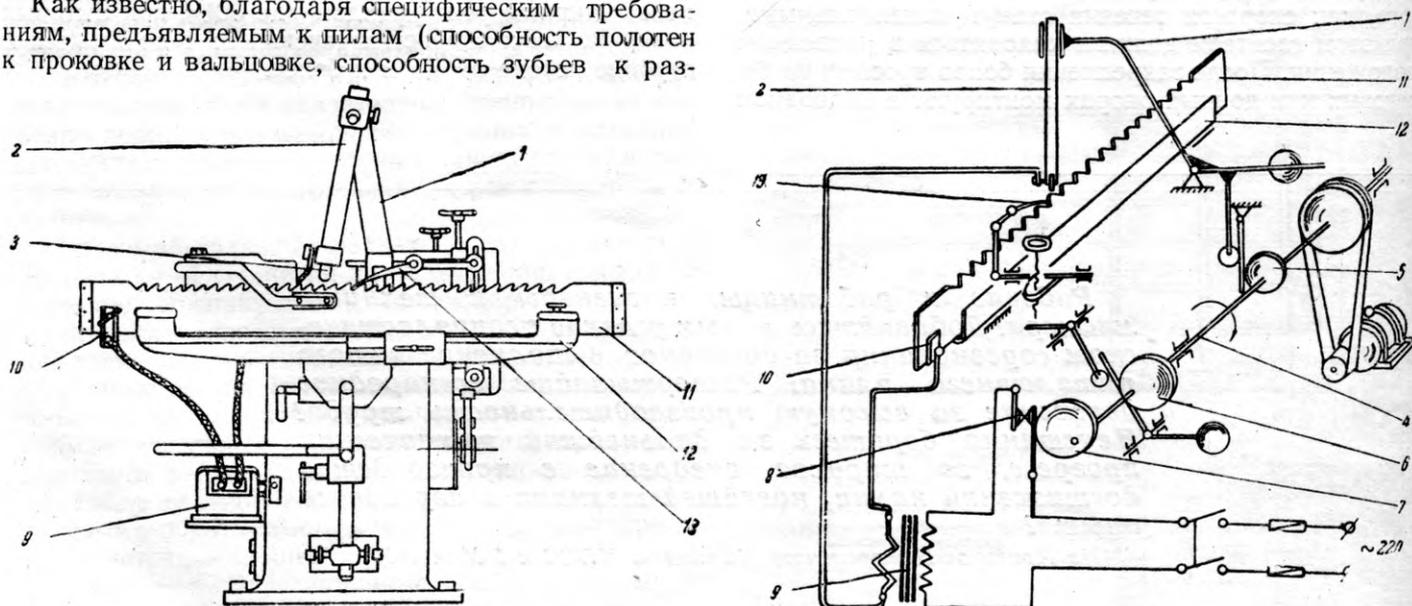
Пилотный автомат ИП-1, приспособленный для электроконтактной закалки зубьев пил: слева—общий вид; справа—кинематическая схема механизма и электрическая схема закалочного устройства
